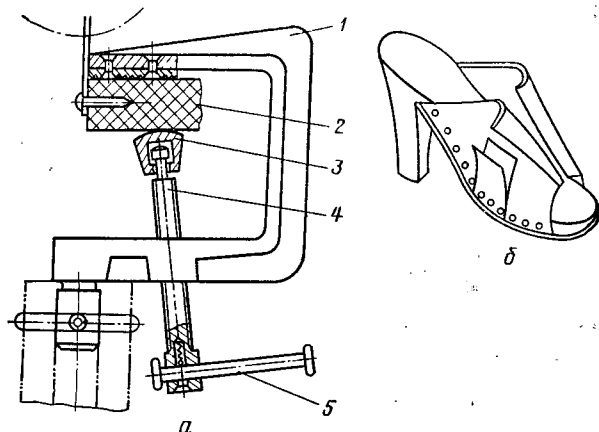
Приспособление к разрывной машине для определения прочности крепления подошвы гвоздебортового метода (а) и схема надрезания образца на заготовке верха обуви (б)
